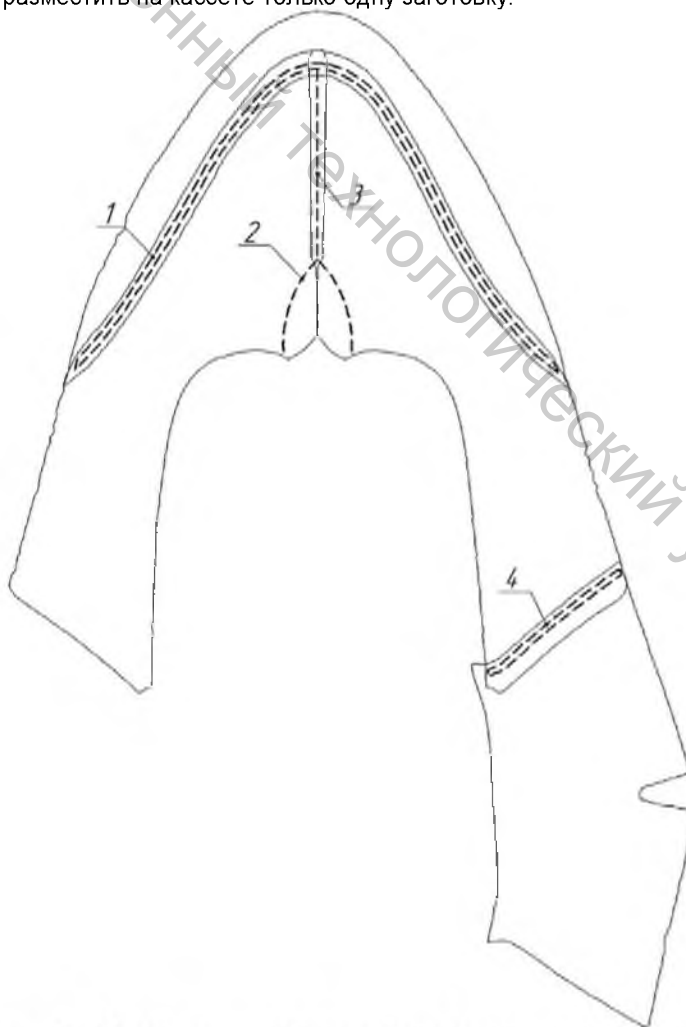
Контур деталей верха обуви и соединительных строчек
